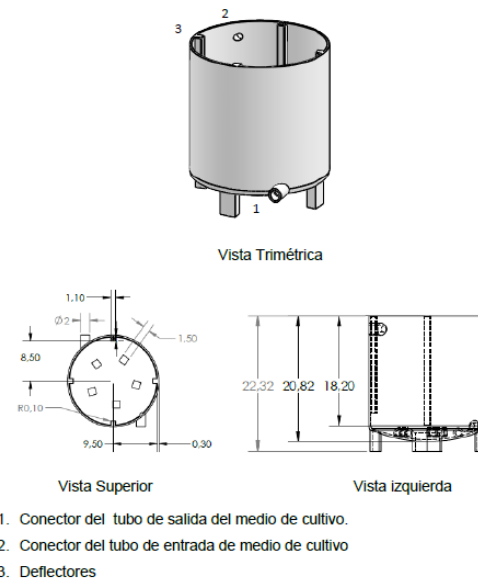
Dimensiones del Reactor (Diseño en SolidWorks2017®)
